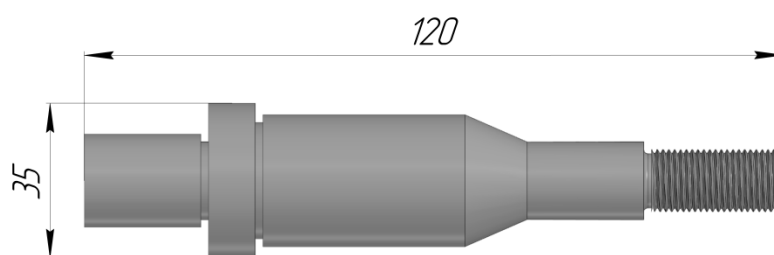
Деталь типу тіла обертання для оброблення на токарному верстаті
